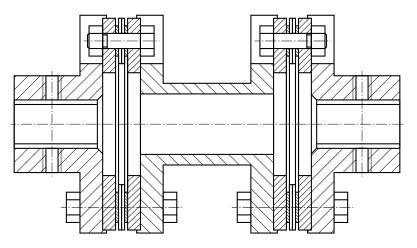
Accouplement à fixation par serrage sur clavettes
